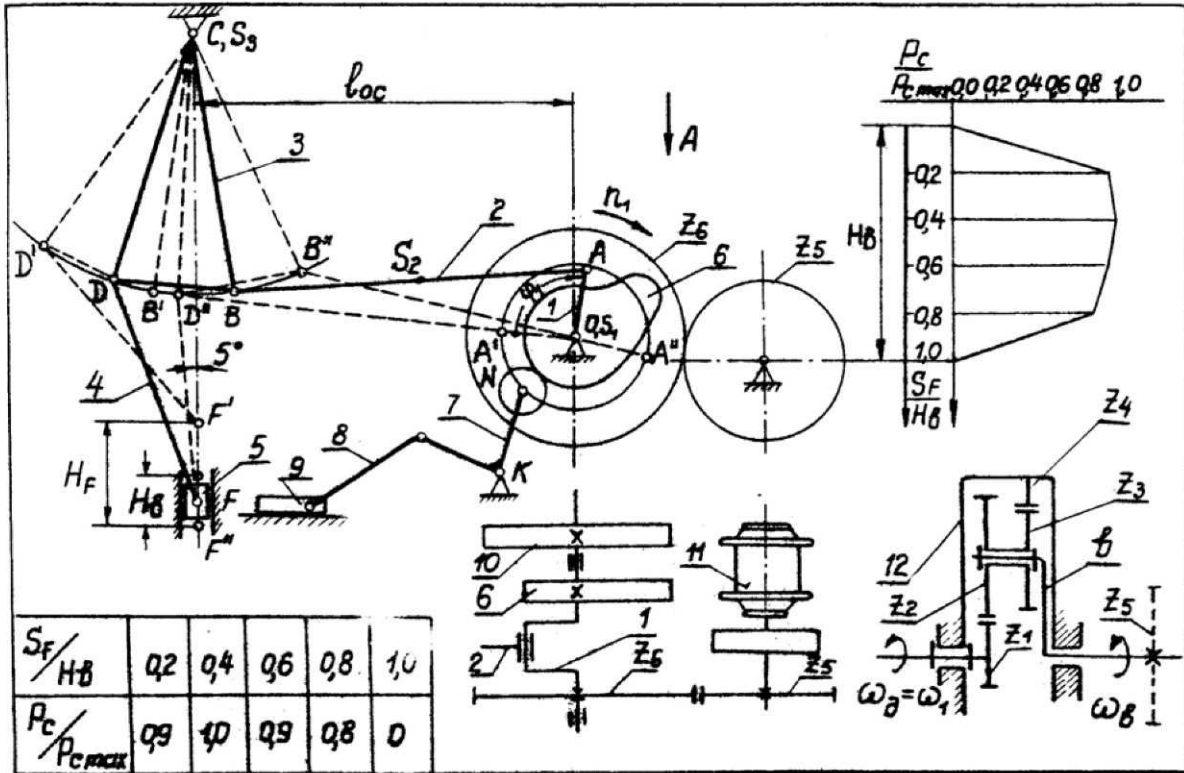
Кривошипно-коленный пресс: механизмы и диаграммы
